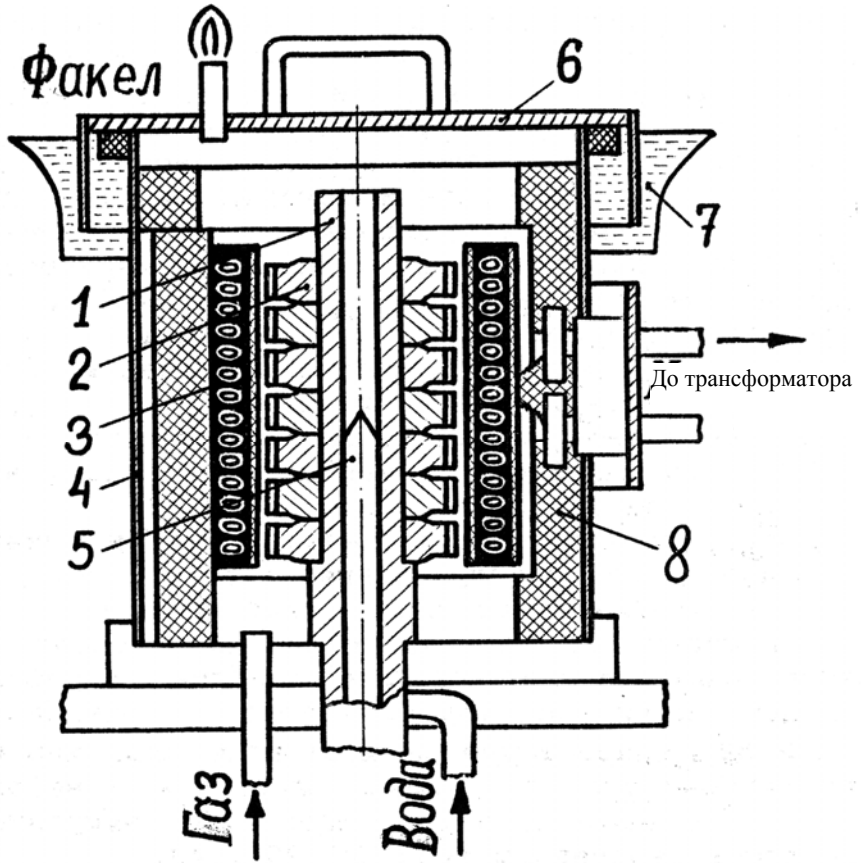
Агрегат періодичної дії для швидкісної цементації з нагріванням струмами високої частоти: 1 - циліндровий стержень; 2 - деталі; 3 – індукційний нагрівач; 4 - кожух печі; 5 – центруючий шпindel; 6 - кришка; 7 - герметичний затвор; 8 - керамічний ізолятор
